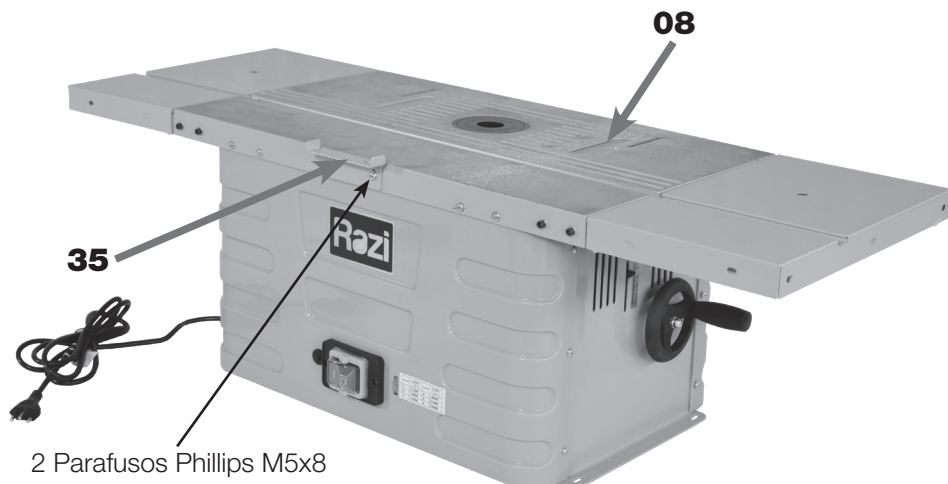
Montagem do Suporte da Barra de Pressão Frontal
